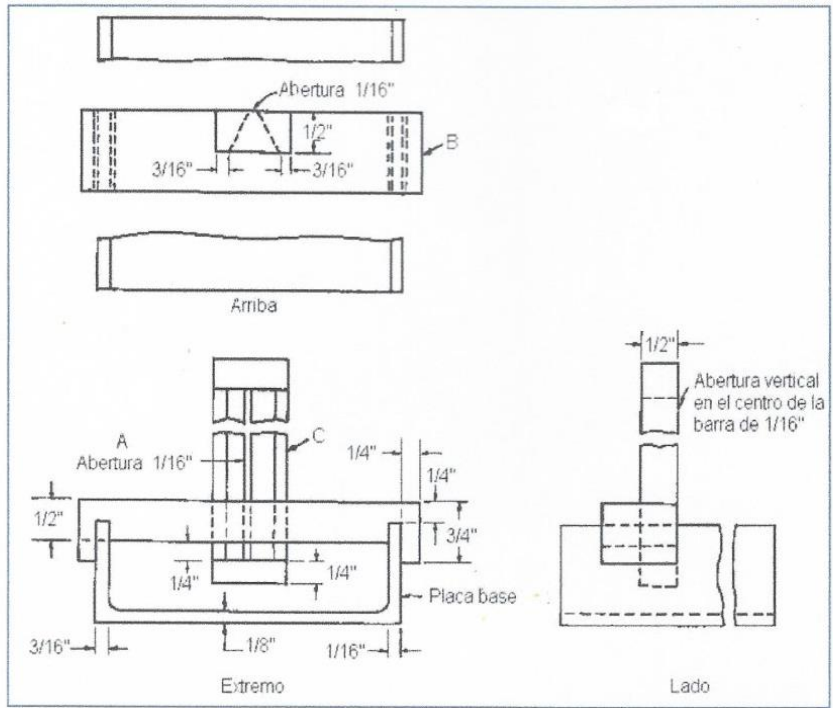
Detalle en planta del equipo adecuado para la determinación del diámetro final usado para el alineamiento del espécimen.
